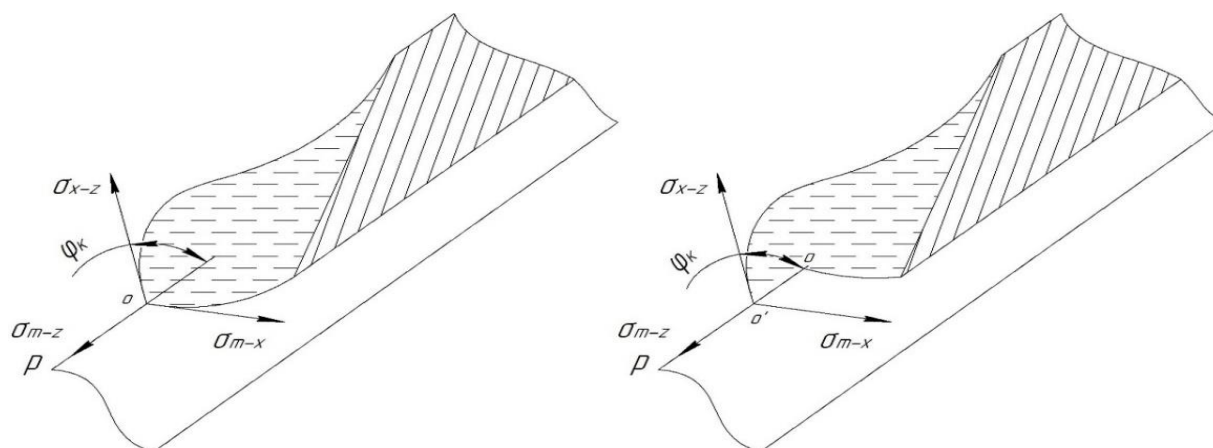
Удержание металла сварочной ванны за счет наличия фронта плавления в головной части сварочной ванны
